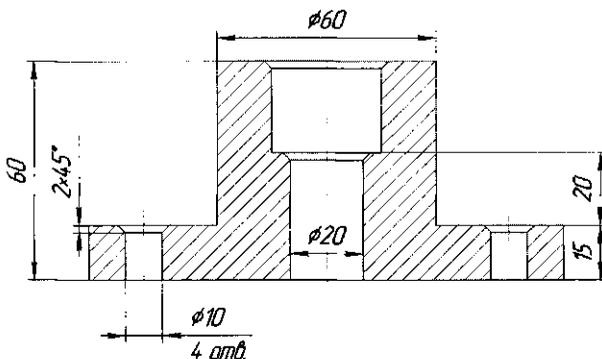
Конечный вид чертежа (вид спереди) с размерными линиями
